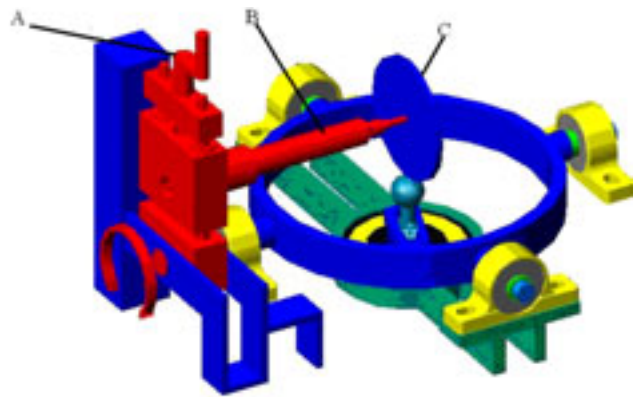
Rotación de la base del tornillo de ajuste de carga: (A) Tornillo de ajuste; (B) Celda de carga; (C) Fresa de deposición.
